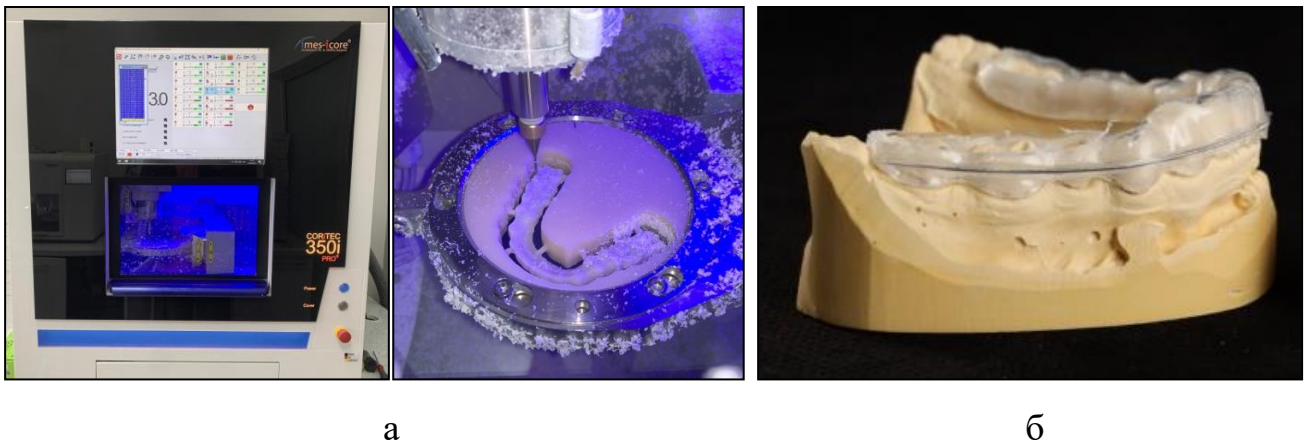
Этапы изготовления (САМ) СОРЦ 2: а - изготовление внутренней части на 5-осевом фрезерном станке Coritec 350i (Imes-Icore) из блока на основе PMMA; б - вид готового СОРЦ 2 на гипсовой модели
